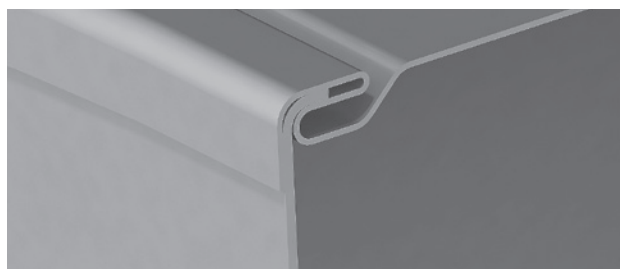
Сборка корпуса вентилятора на «питтсбургском фальце»
